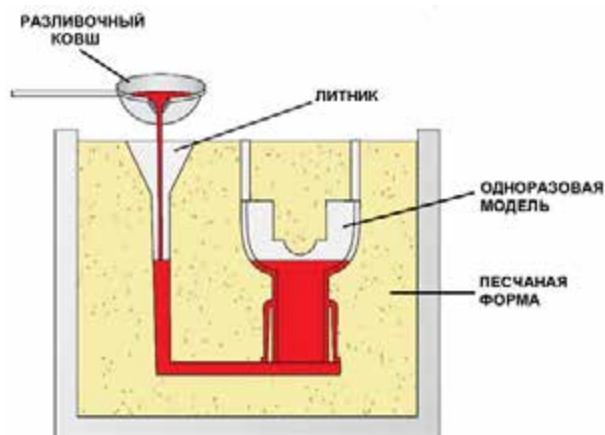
ro-06: Схематическое изображение установки для литья в песчаную форму; источник: MSI
